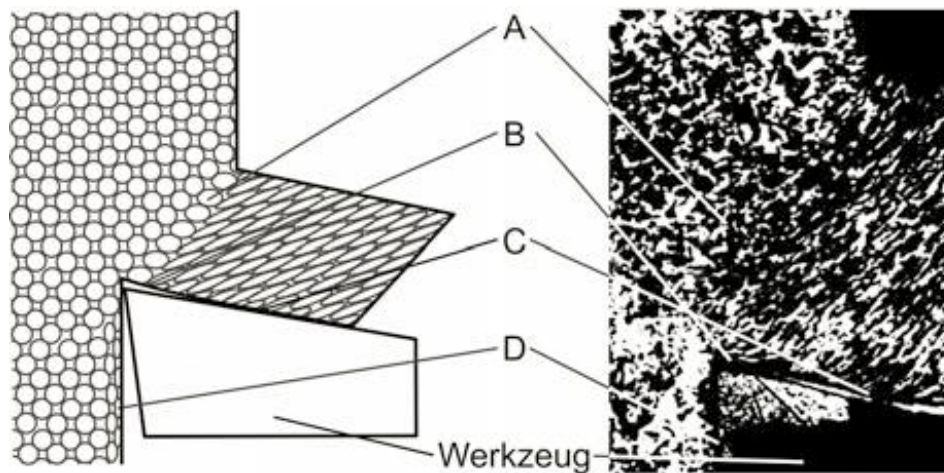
Spanbildung und Spanstruktur; Quelle: Zerspanung der Eisenwerkstoffe, Stahleisen-Bücher
